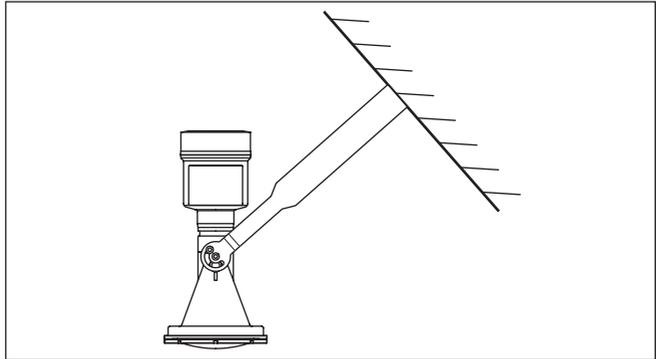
Montaje en pared oblicua mediante el estribo de montaje con una longitud de 300 mm
